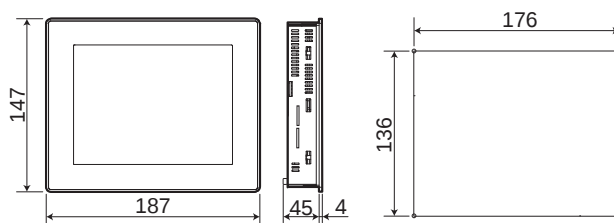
Габаритный чертеж и схема разъема для терминала управления оператора (размеры в мм)
